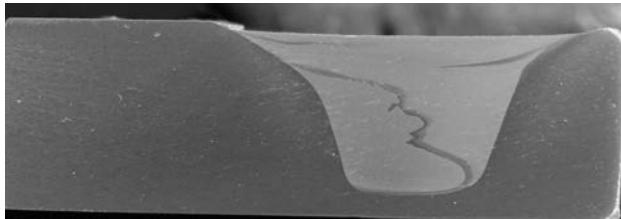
Макрошлиф образца сплава 6082 после сварки в воде
